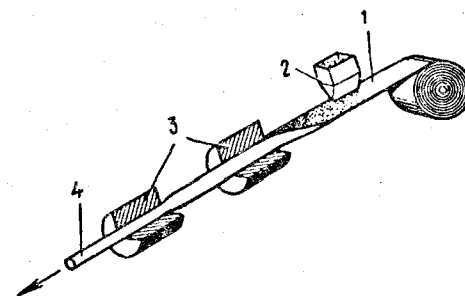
Схема изготовления порошковой проволоки: 1 — стальная лента; 2 — бункер с шихтой; 3 — фильеры; 4 — порошковая проволока
